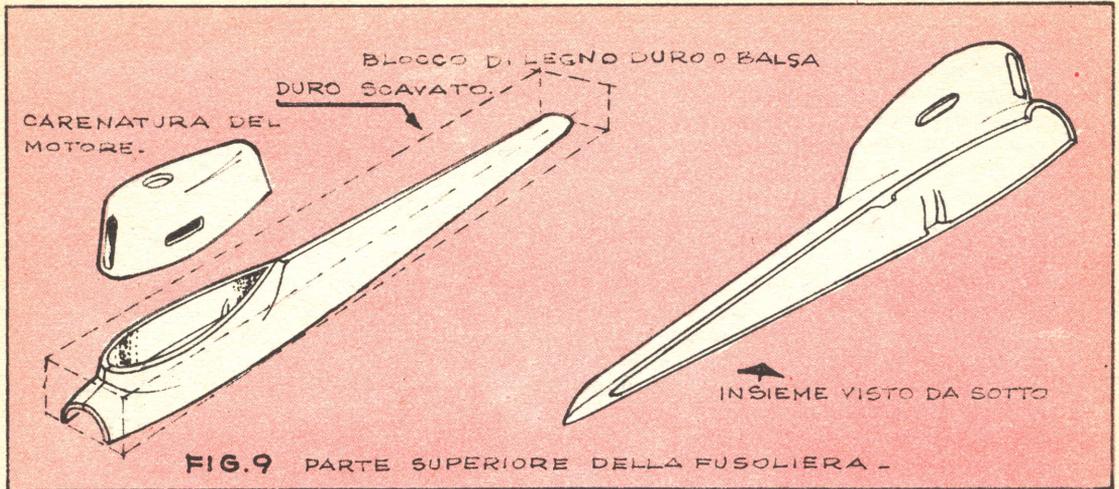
PARTE SUPERIORE DELLA FUSOLIERA -
